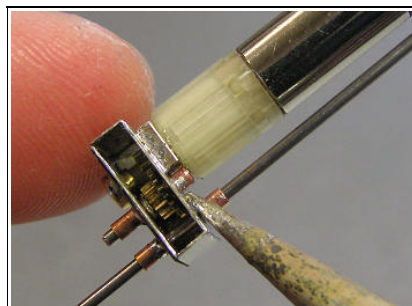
Bei erfolgreichem Testlauf kann die Buchse mit eingesteckter Welle am Getriegehäuse angelötet werden.
